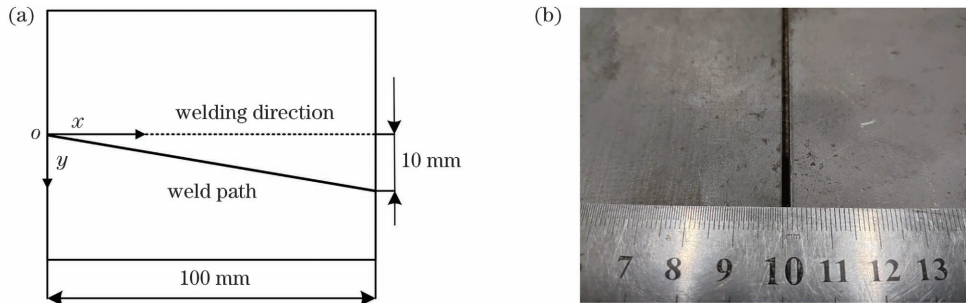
焊缝路径识别试验方案。(a) 焊接方向与焊缝路径; (b) 对接焊缝实物图
